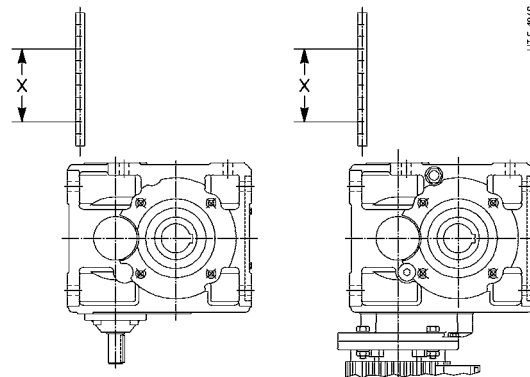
Позиционировать цилиндрический редуктор или мотор-редуктор в конструктивном исполнении V7 для измерения уровня (количества) масла.
